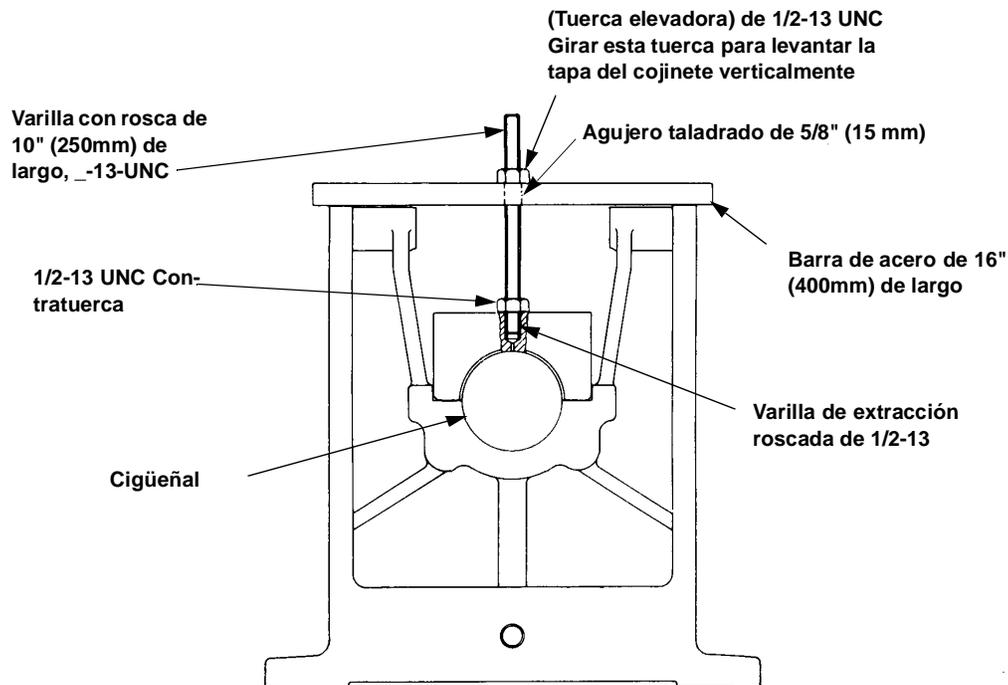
EXTRACTOR DE TAPA DE COJINETE
